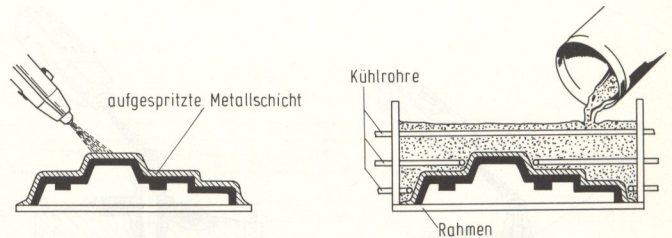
Herstellen eines Werkzeugs für die PUR-Verarbeitung mit einer Metallegierung (Schmelzbereich 390 bis 410 °C)
